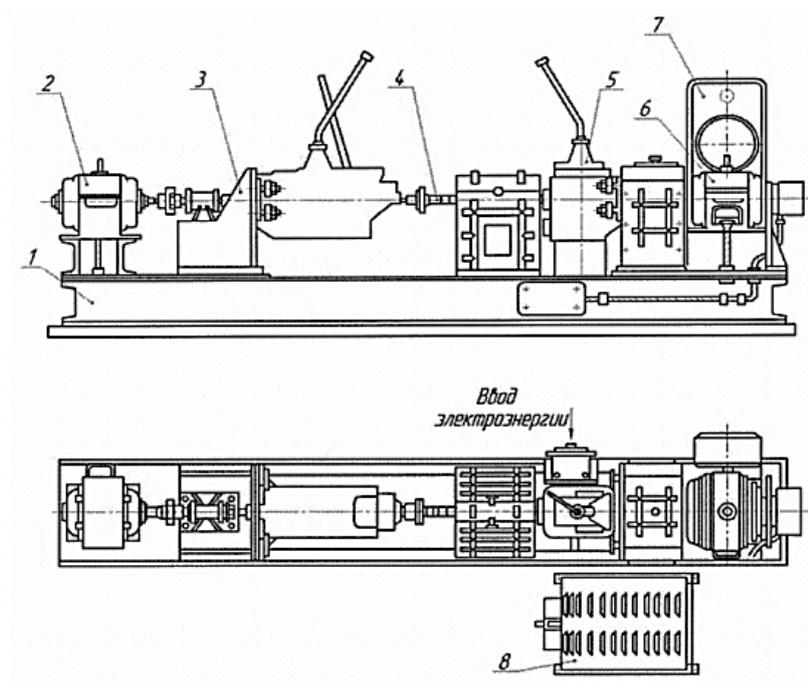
Стенд для испытания коробок передач, ГОСНИТИ модель 5027
